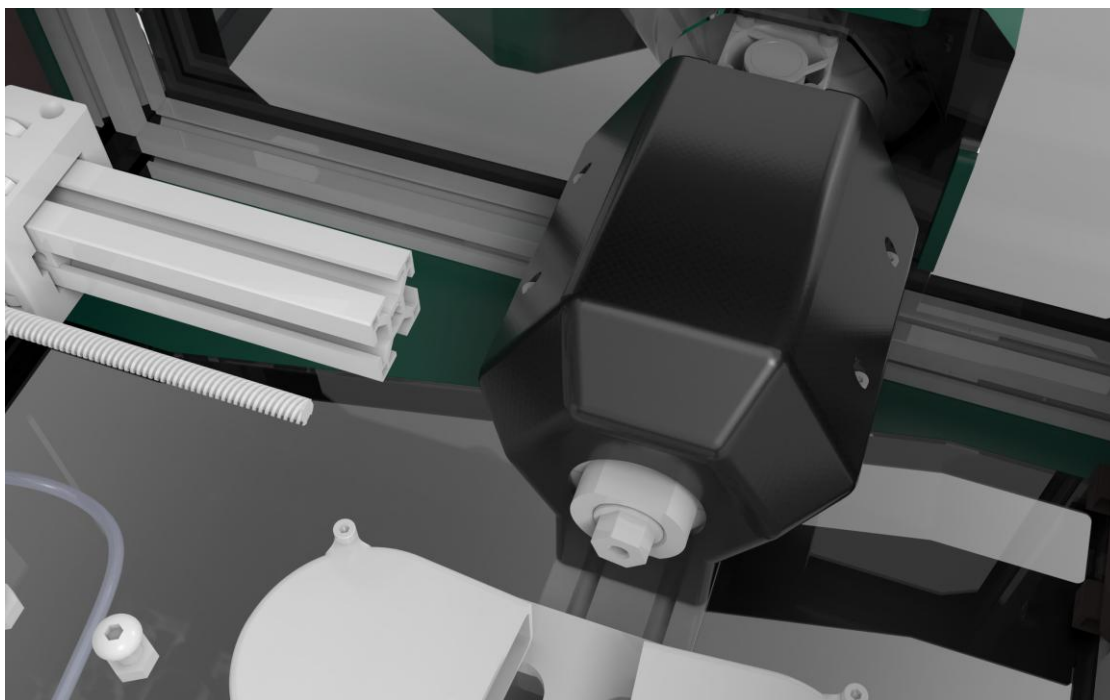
Detailní pohled na perforovaná místa krytu (výdechy) a spodní ventilační mřížky (vstup vzduchu)
